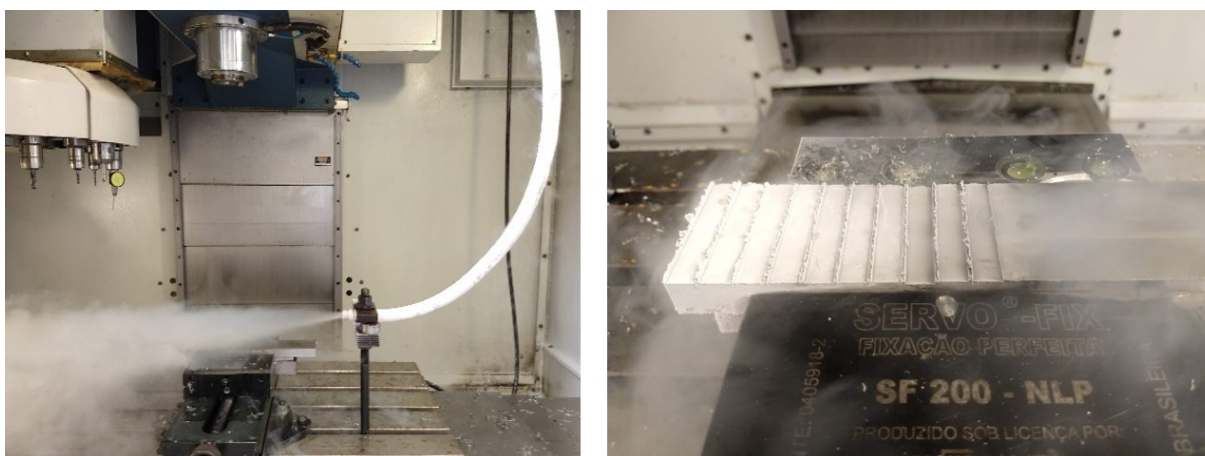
Centro de Usinagem CNC ROMI D600 – Instituto Mauá de Tecnologia
